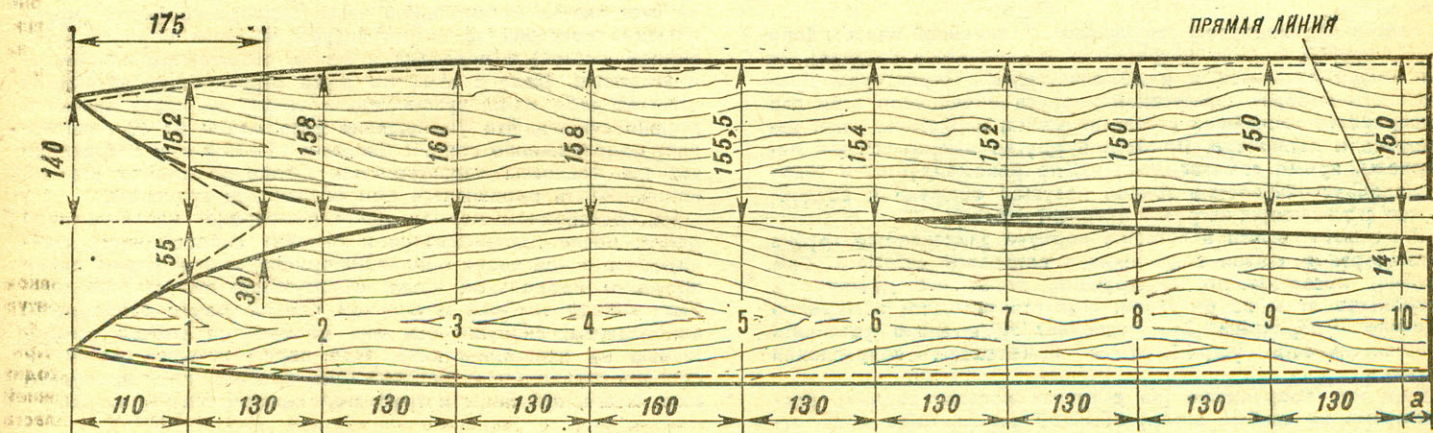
Основные размеры раскроя листа фанеры для изготовления корпуса (размер «а» определить после сборки корпуса).
